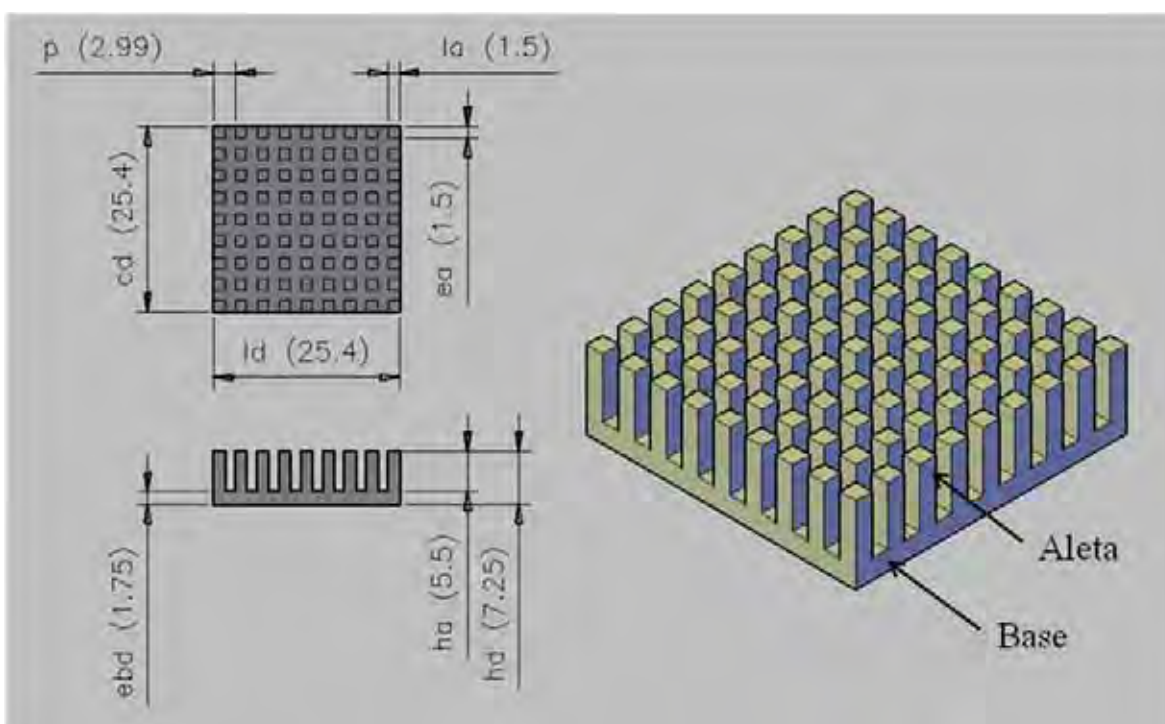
Dimensões do dissipador de calor com 81 pinos (9x9) de seção quadrada.
